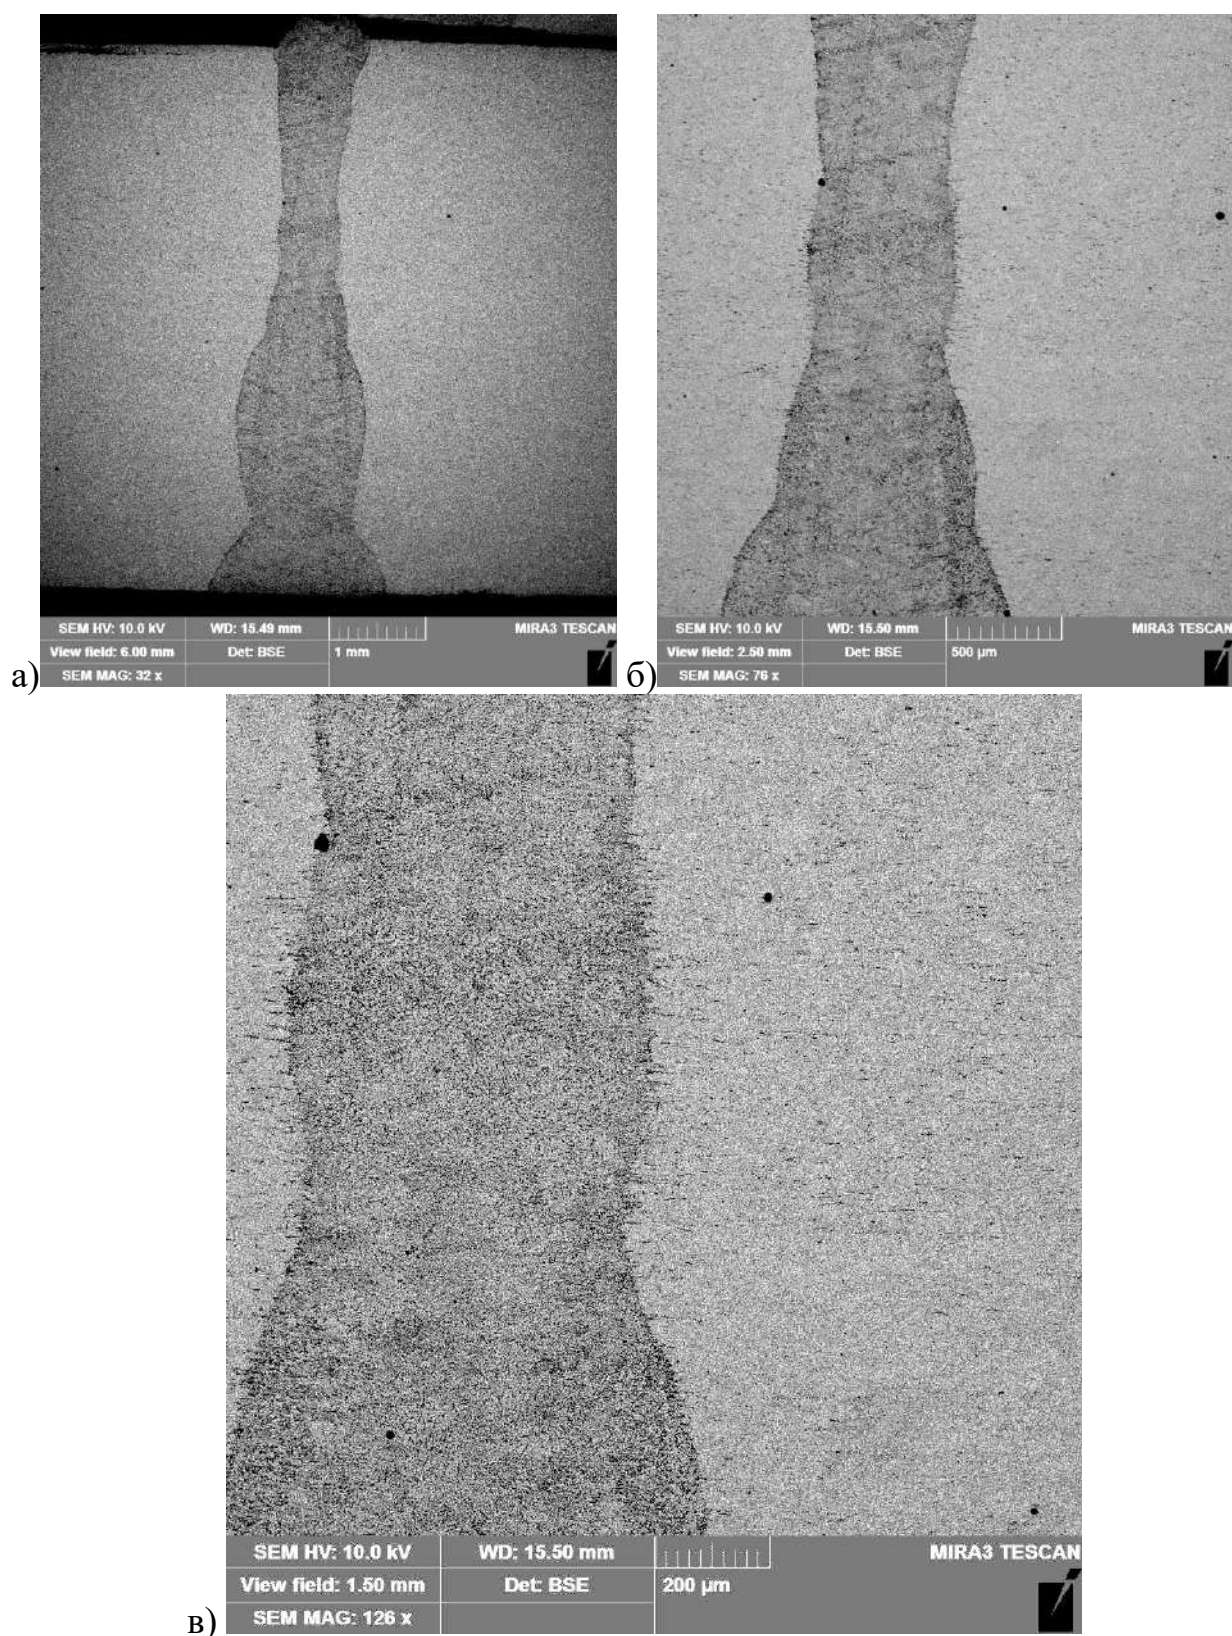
Мікроструктура металу зварного з'єднання (6 мм), що отримано лазерним зварюванням: а – загальний вигляд зварного шва; б, в – середня частина шва при різних збільшеннях.
